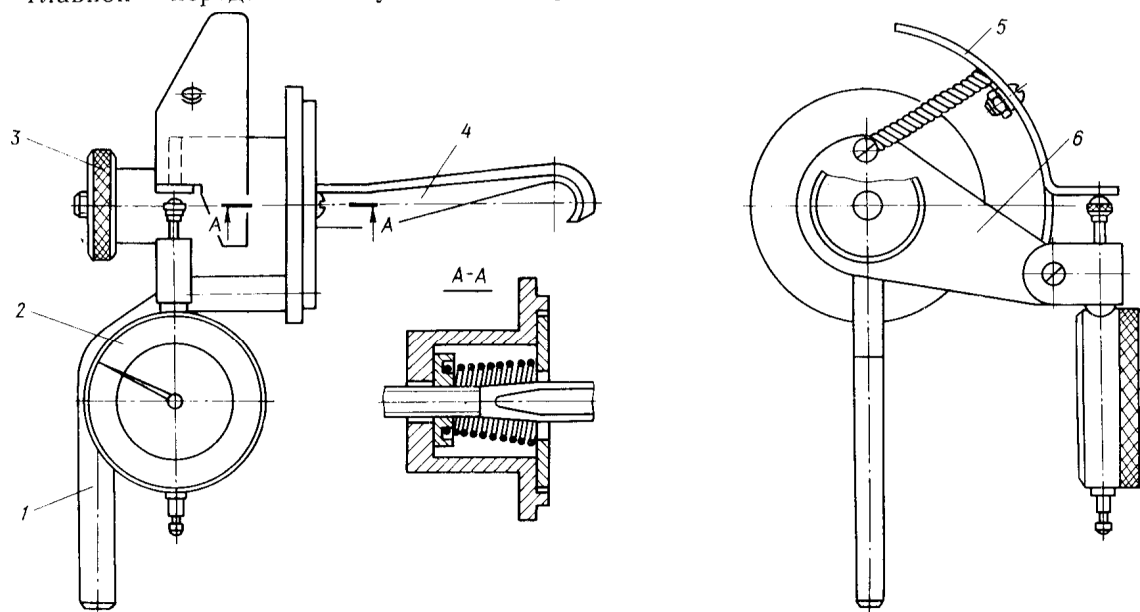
Контрольное приспособление для проверки зазора в шестернях главной передачи:
